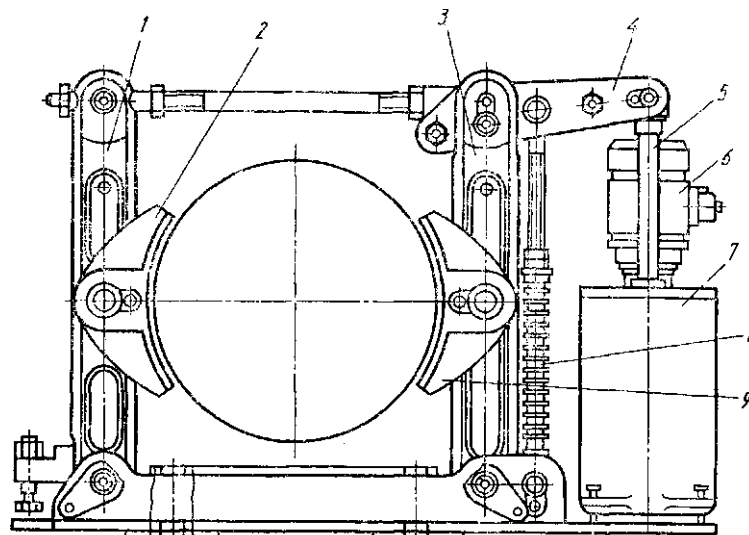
Колодочный пружинный тормоз с электрогидротолкателем
